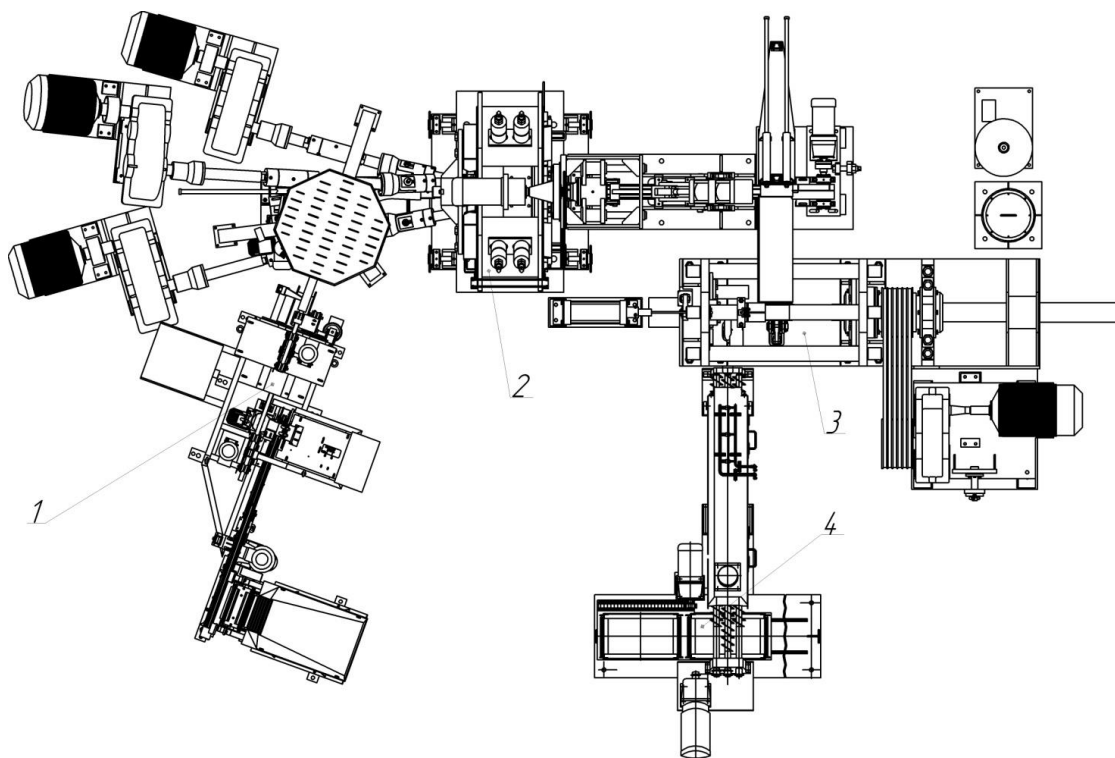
Состав оборудования линии АЛВП: 1 – нагревательное устройство; 2 – трехвалковый стан винтовой прокатки; 3 – калибровочный пресс; 4 – камера контролируемого охлаждения
